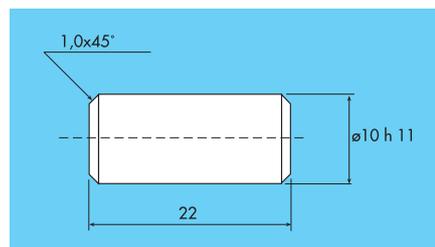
Pino cilíndrico, usinado conforme plano de trabalho da fig. 12
